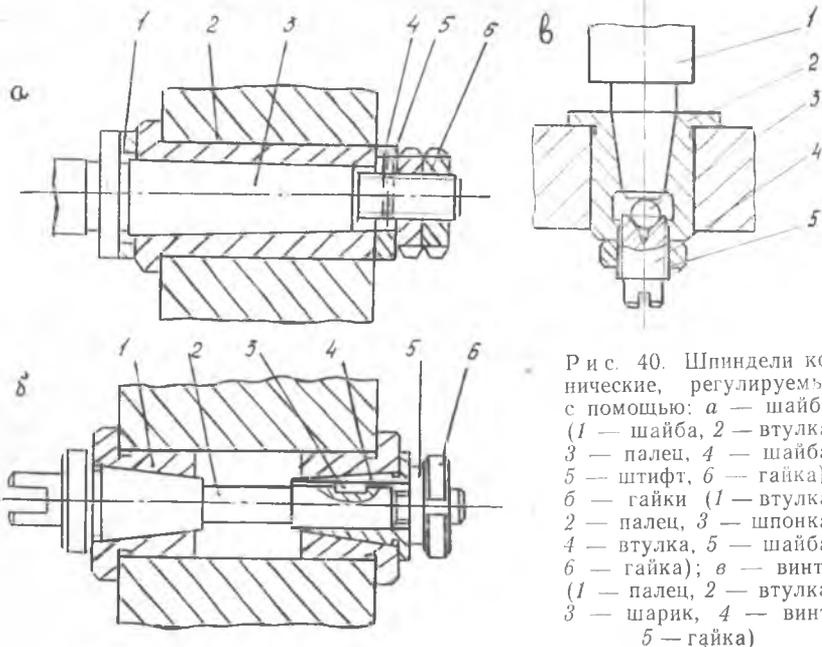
Шпиндели конические, регулируемые с помощью: а — шайбы (1 — шайба, 2 — втулка, 3 — палец, 4 — шайба, 5 — штифт, 6 — гайка); б — гайки (1 — втулка, 2 — палец, 3 — шпонка, 4 — втулка, 5 — шайба, 6 — гайка); в — винта (1 — палец, 2 — втулка, 3 — шарик, 4 — винт, 5 — гайка)
